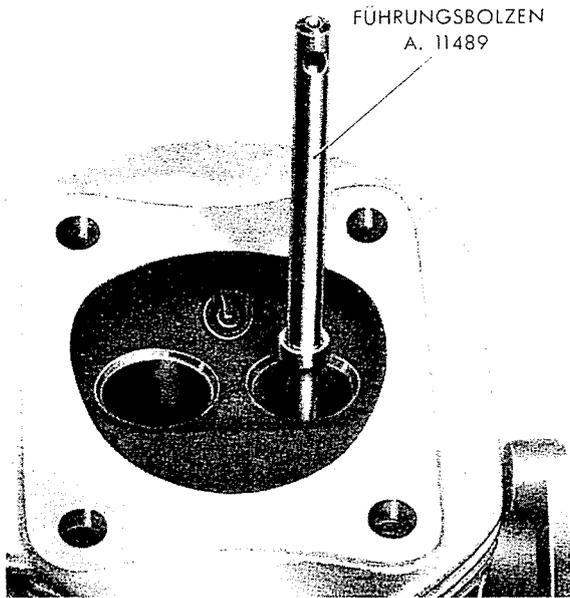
Führungsbolzen A. 11489 für die Schleif- und Fräsvorrichtung bei der Nacharbeit der Ventilsitze.
